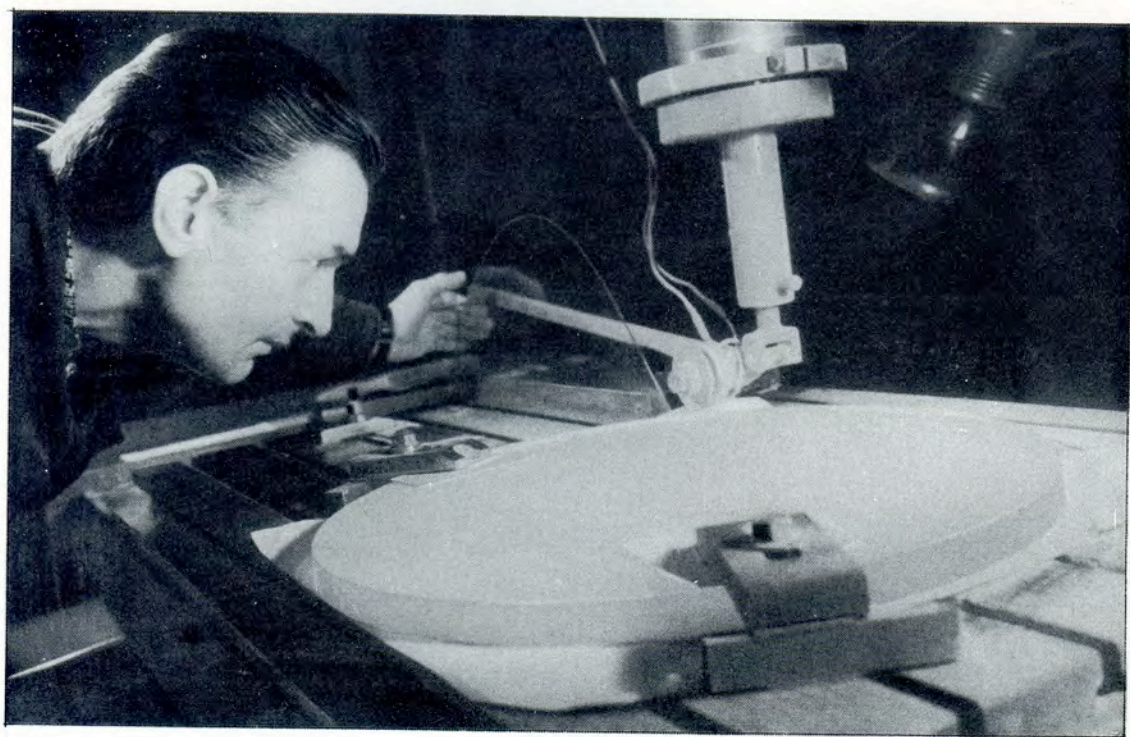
Изготовление раstra для 2-метровой жидководородной камеры.
